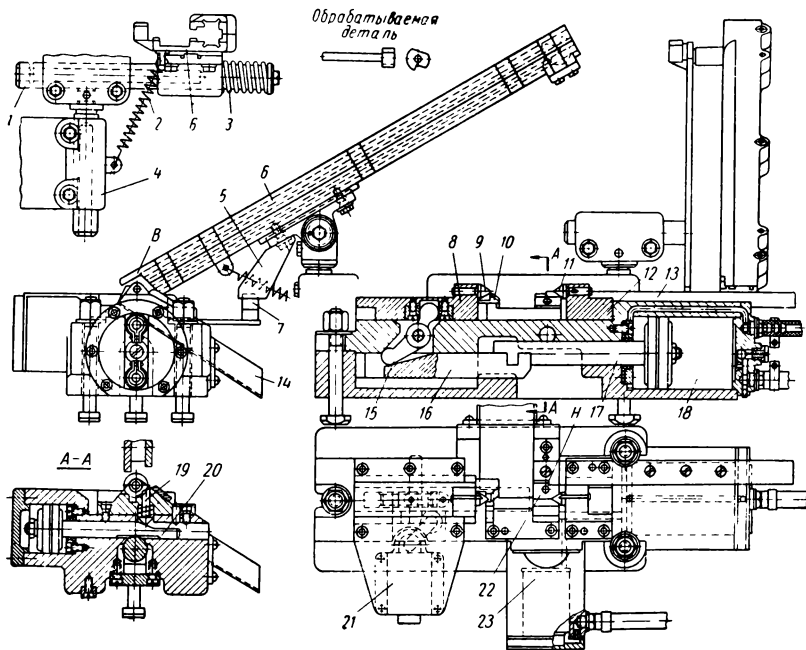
Загрузочное устройство для фрезерования деталей, закрепленных в центрах
